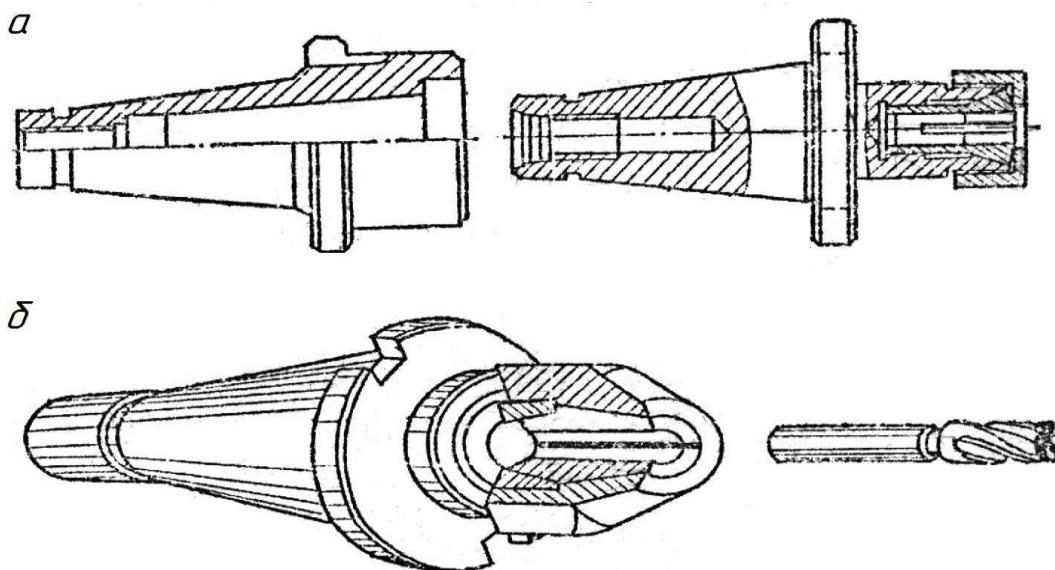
Крепление фрез с цилиндрическим хвостовиком: а – в цанговом патроне; б – в кулачковом патроне
